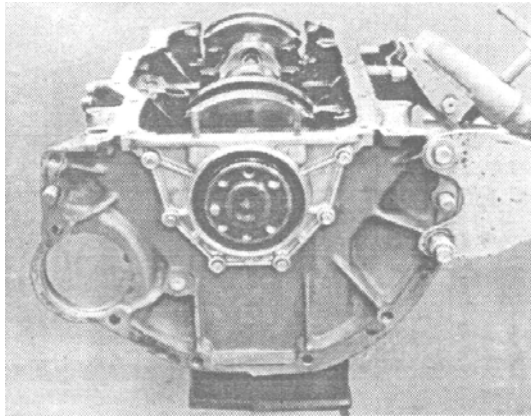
Установка держателя заднего сальника коленчатого вала
